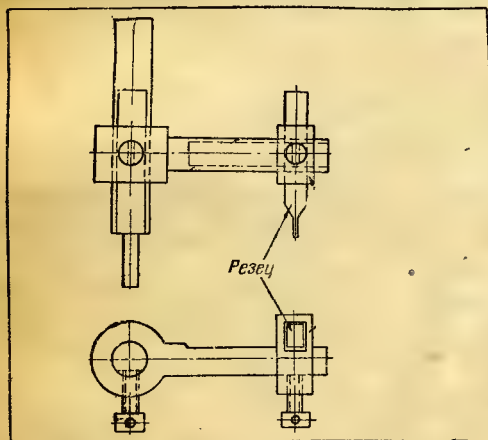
Приспособление для сверления больших отверстий на сверлильном станке
